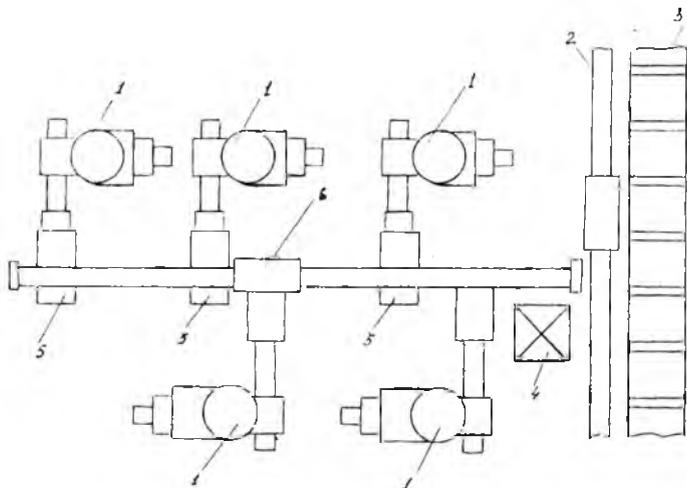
РТК для механической обработки корпусных деталей: 1 — обрабатывающий центр ИР-500МФ4; 2 — автоматический штабелер; 3 — ячейки автоматизированного склада; 4 — поворотный стол; 5 — магазин-накопитель; 6 — ПР
